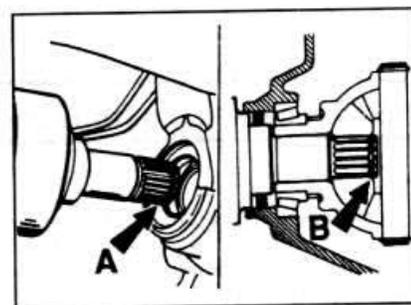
Расположение стопорного кольца при установке внутреннего шарнира приводного вала.
